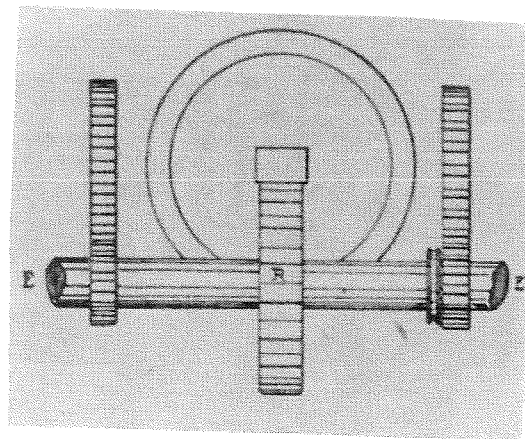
Vista in pianta del meccanismo di trasmissione del movimento.
